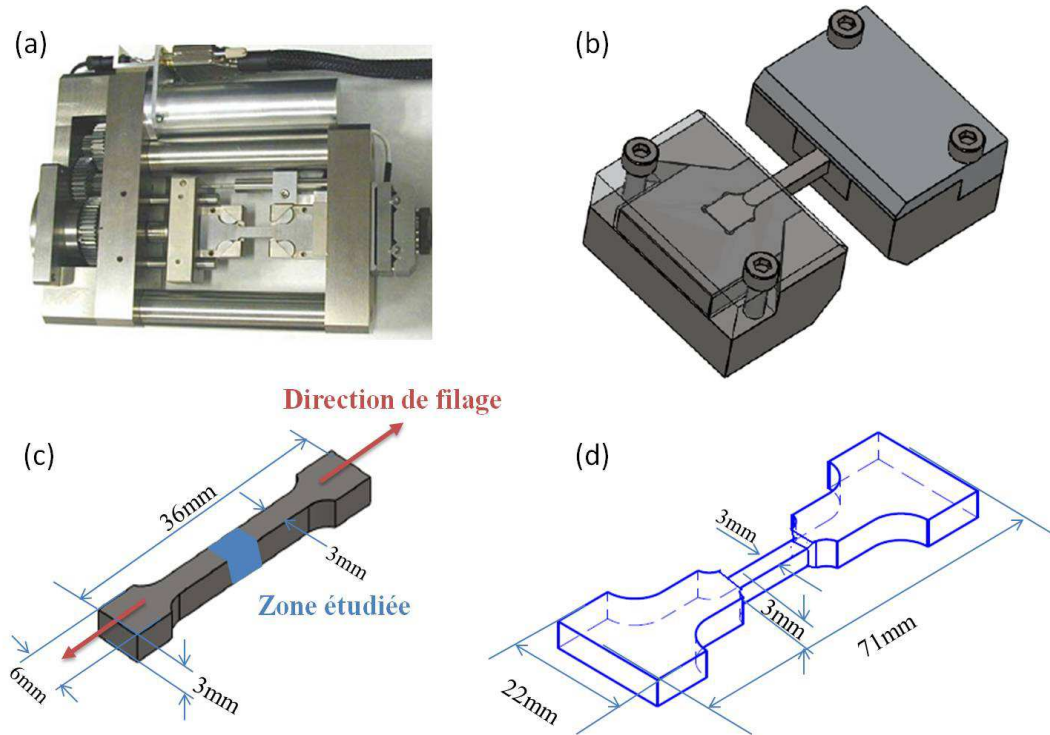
(a) Photographie de la machine de traction adaptable sur 6T1; (b) système d'adaptation pour petites éprouvettes; (c) géométrie des éprouvettes courtes ; (d) géométrie des éprouvettes de taille normale.
